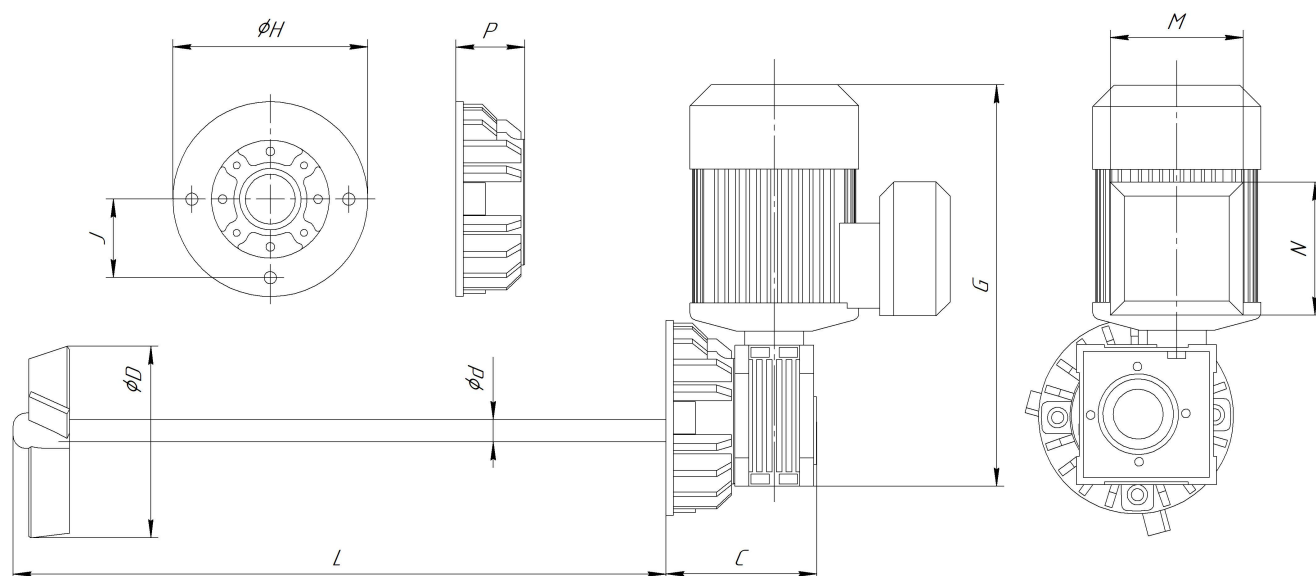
Габаритные и присоединительные размеры мешалок SM
